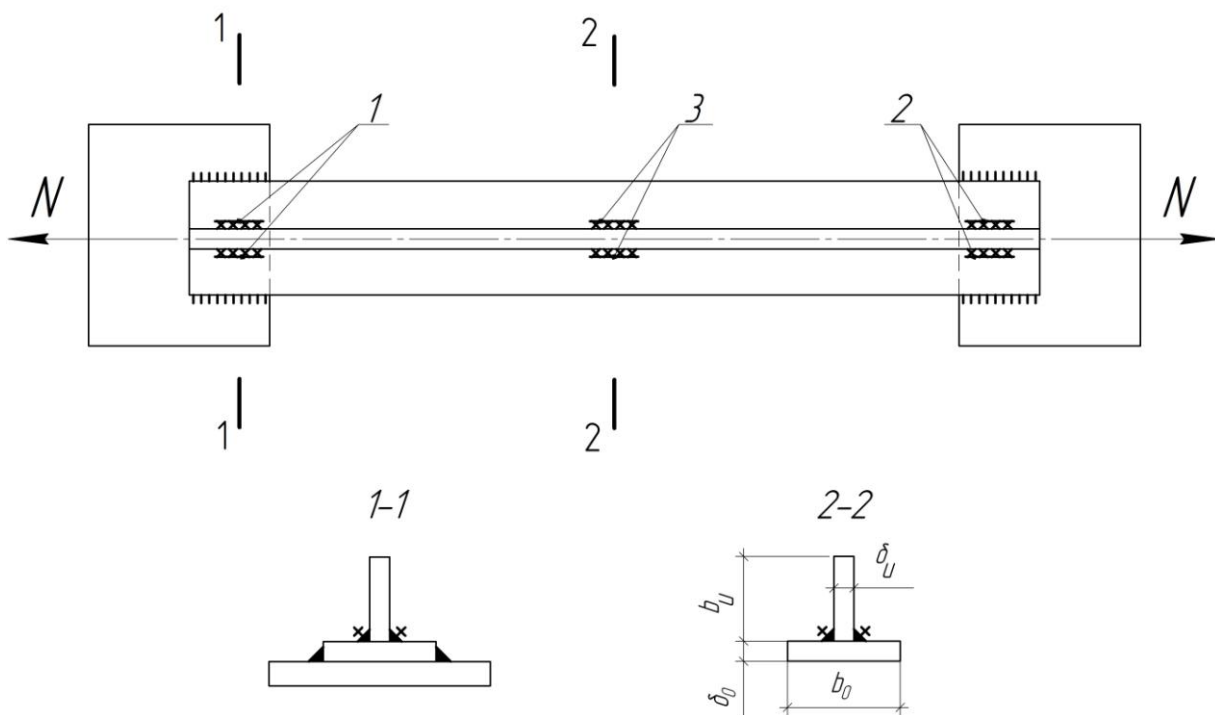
К вопросу о порядке наплавки сварных швов
